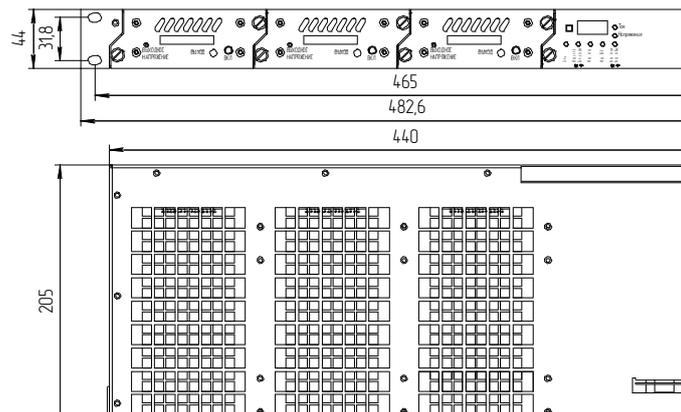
Габаритный чертеж УЭП-2К
